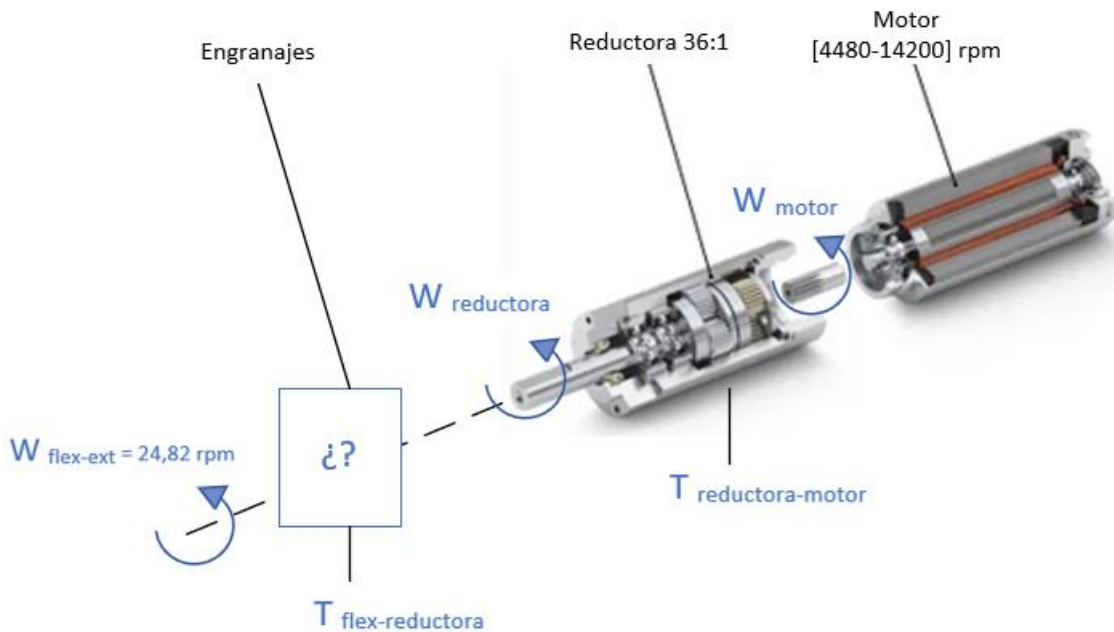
Esquema Motor RE8 + Reductora + Engranajes. [28]
